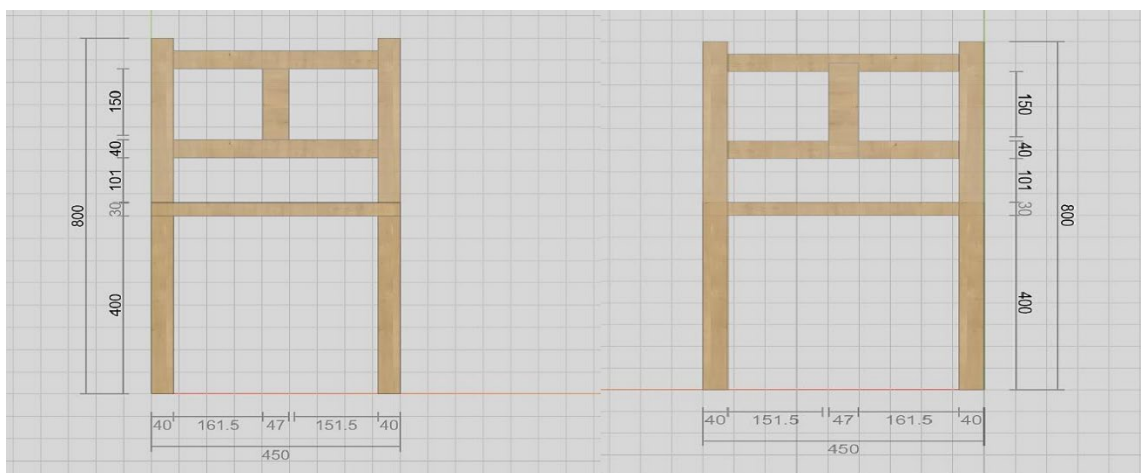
Vederea din frontală și din spate (Front view și Back view)
